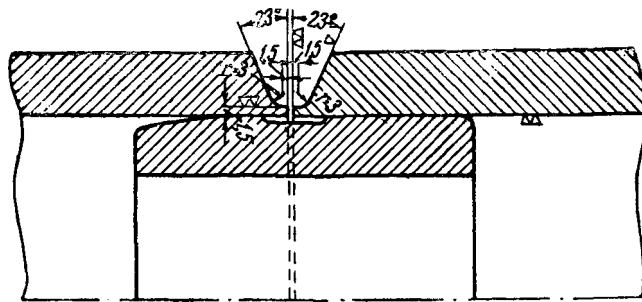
Подготовка труб под сварку встык с медным кольцом.
